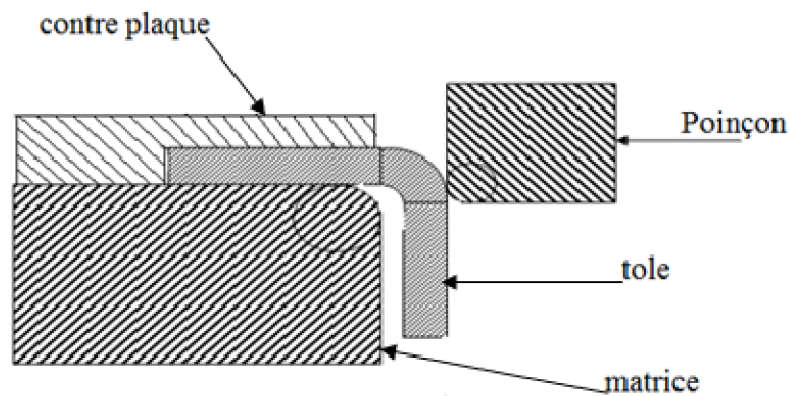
Exemple d'Outil de Cambrage en Équerre.
